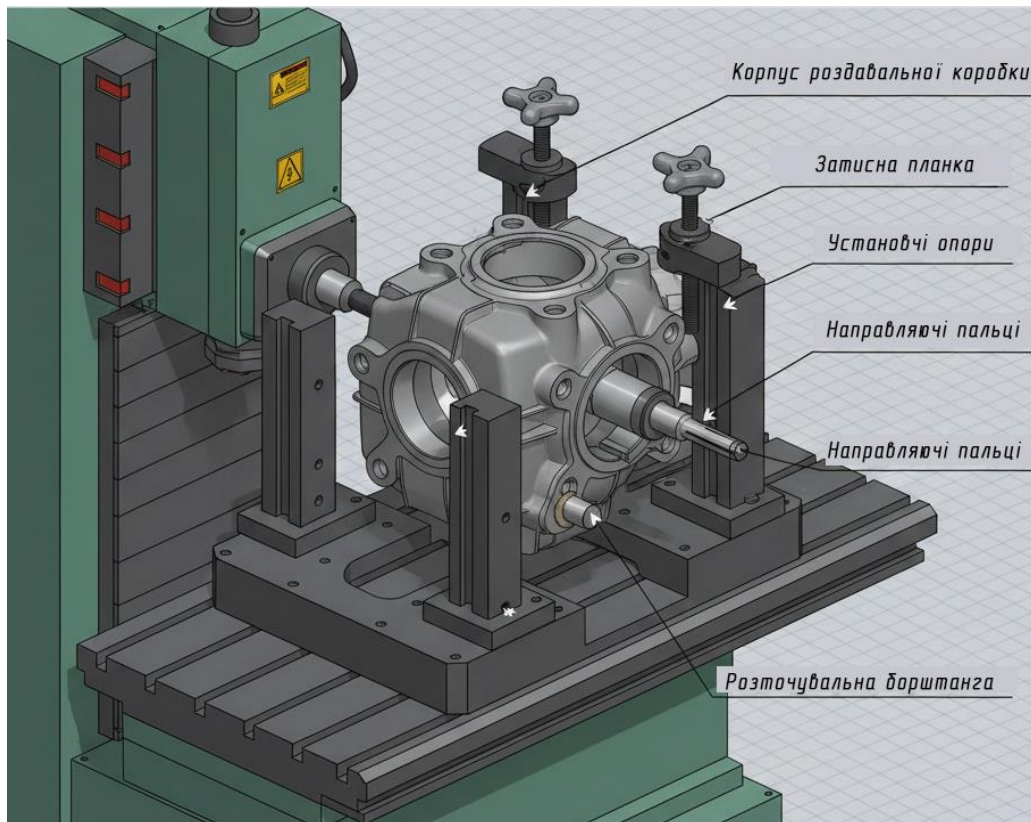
Загальний вигляд пристрою для розточування корпусу роздавальної коробки
